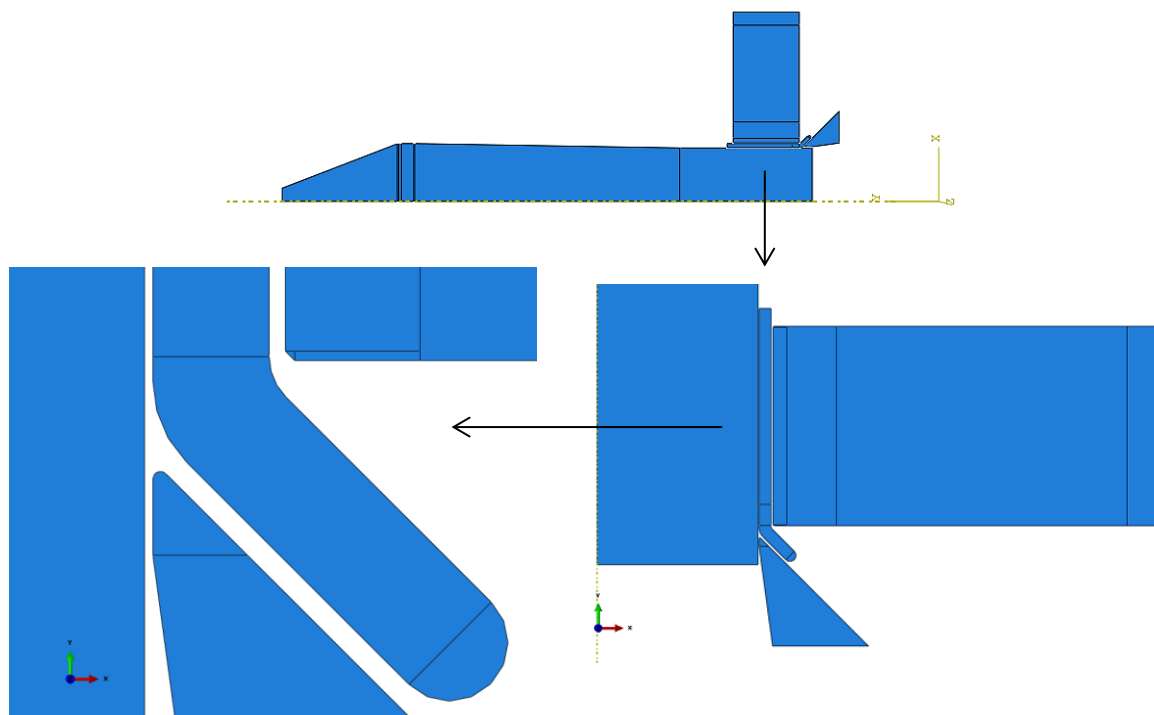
Assemblage des composants en vue d'effectuer l'expansion à froid.
